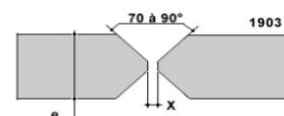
Classification par type de soudage (Soudage MIG/MAG)
